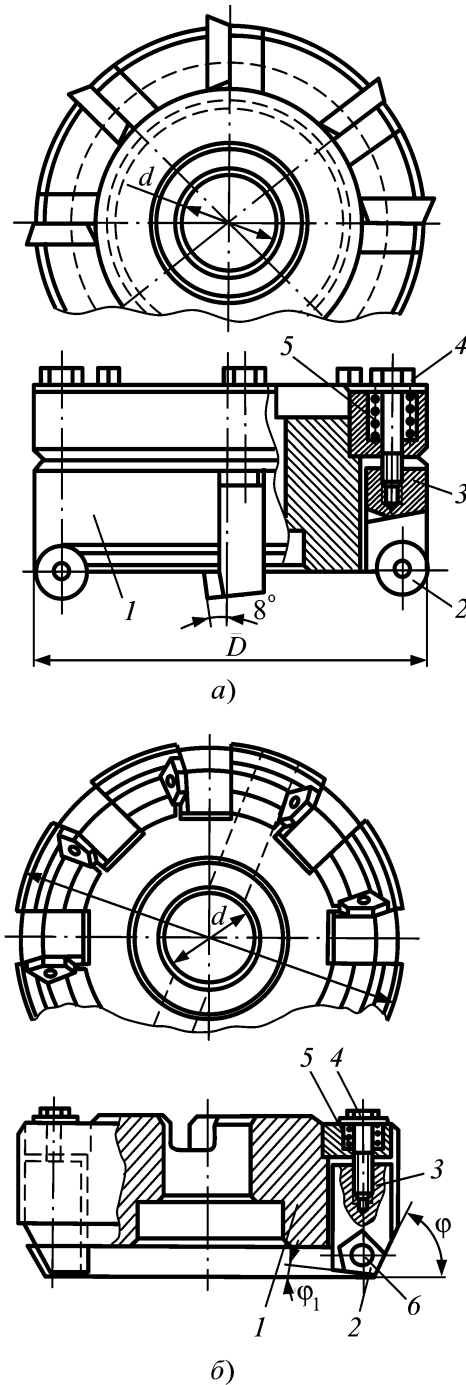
Клиновое крепление зубьев торцовой фрезы
